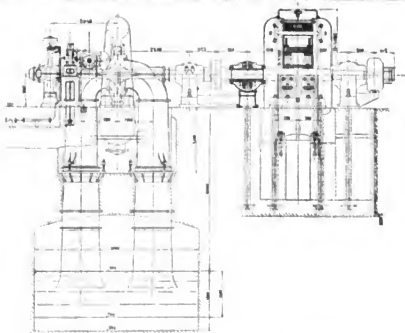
Turbinenseite einer 6000 PS-Maschinengruppe Manojlovac.
